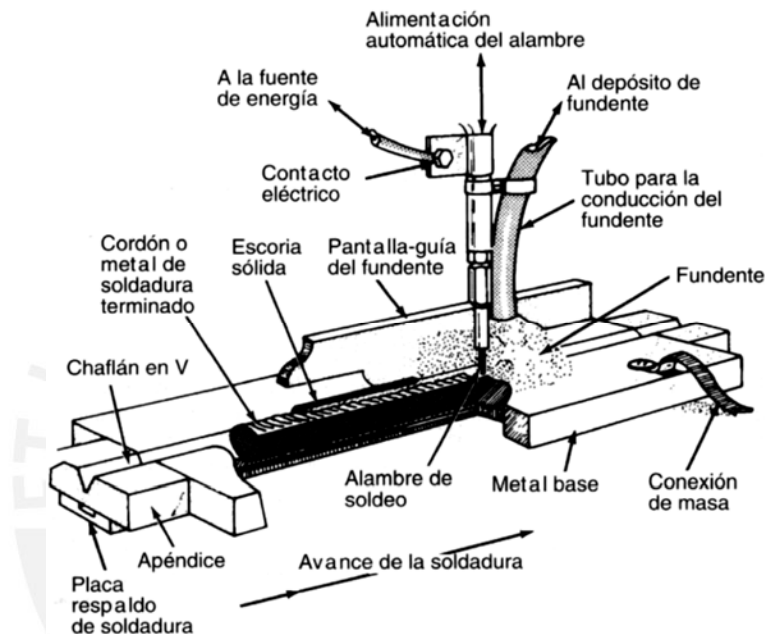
Proceso de soldadura SAW [1]
